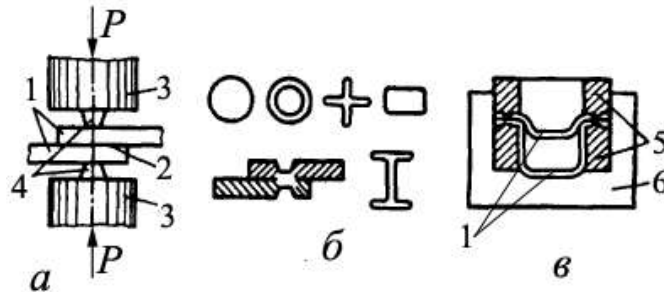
Схеми холодного точкового зварювання і види зварних точок
